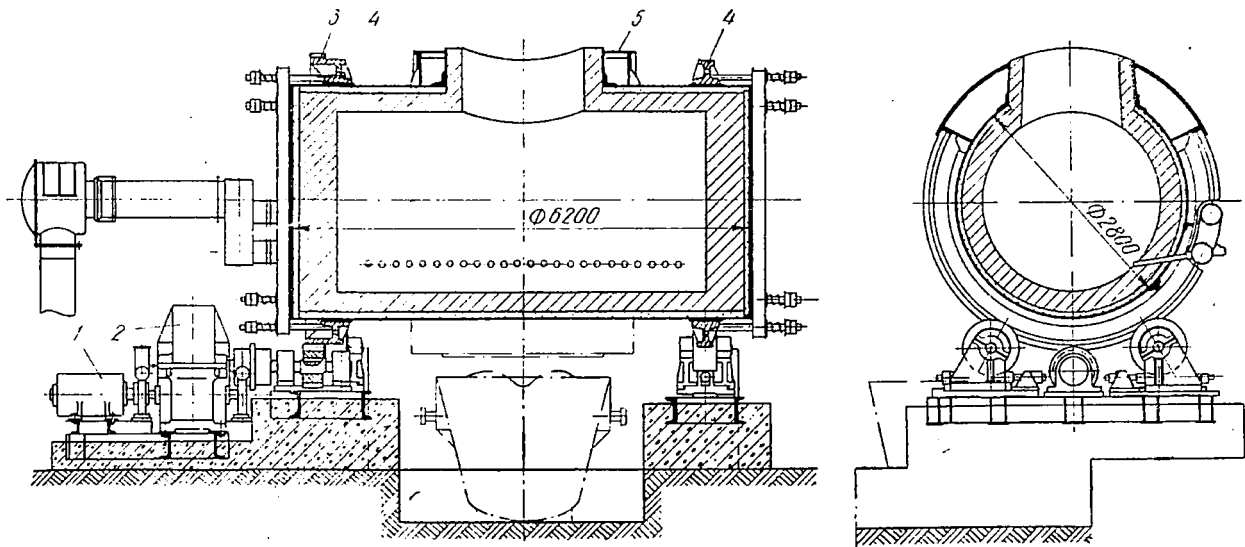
Горизонтальный конвертер для переработки никелевого штейна
